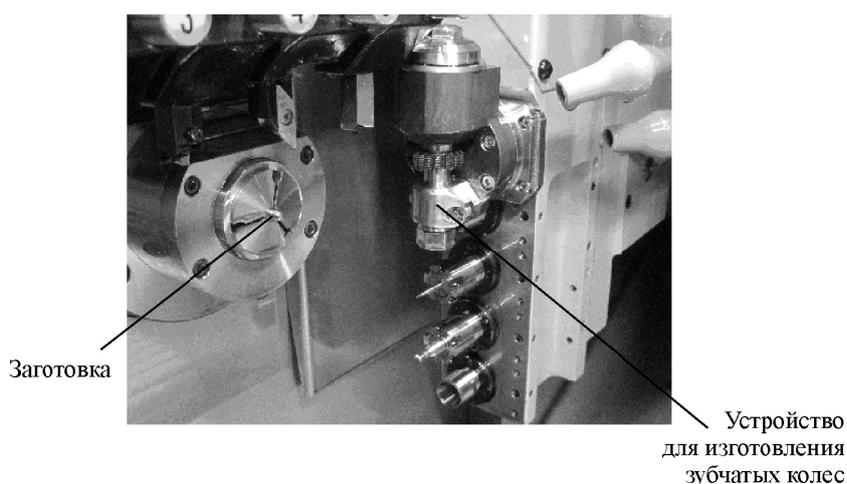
Устройство для изготовления зубчатых колес, установленное на станок
